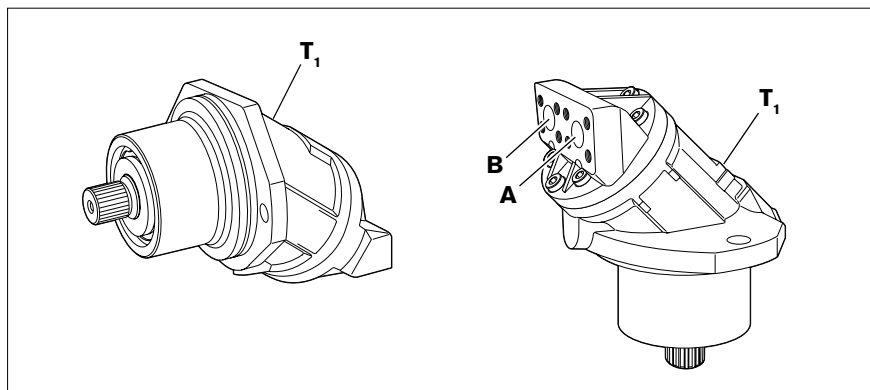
Vue d'ensemble des raccords A2FE, dimension nominale 28 à 180, plaque de raccordement 10, raccords de service en bas
